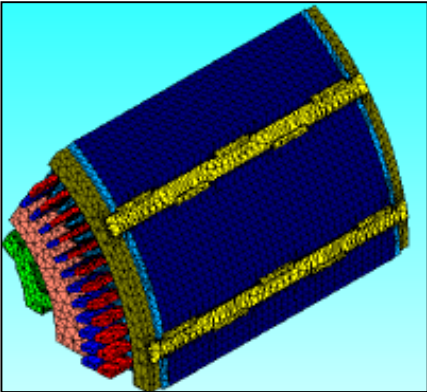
Vista em corte da máquina com tirantes embutidos soldados
